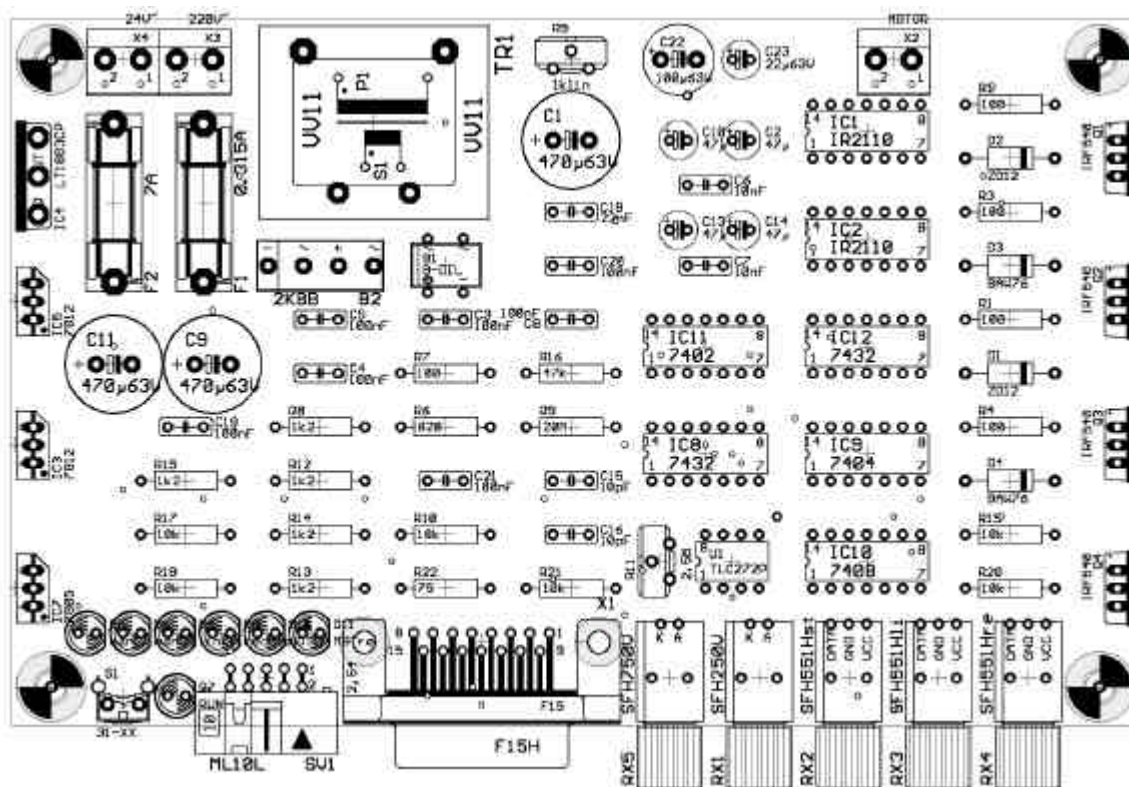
Leiterplatte des Motorsteuerungsgerätes mit zu bestückenden Bauelementen.
